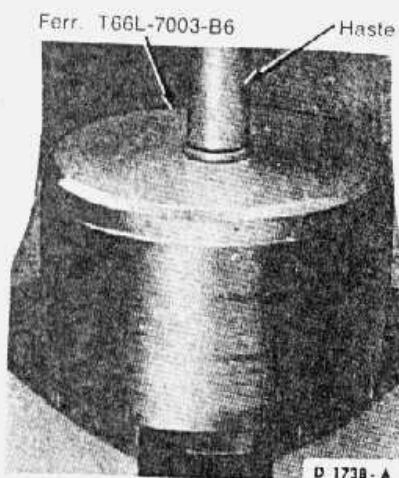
instalação da bucha do tambor da cinta de ré e baixa
